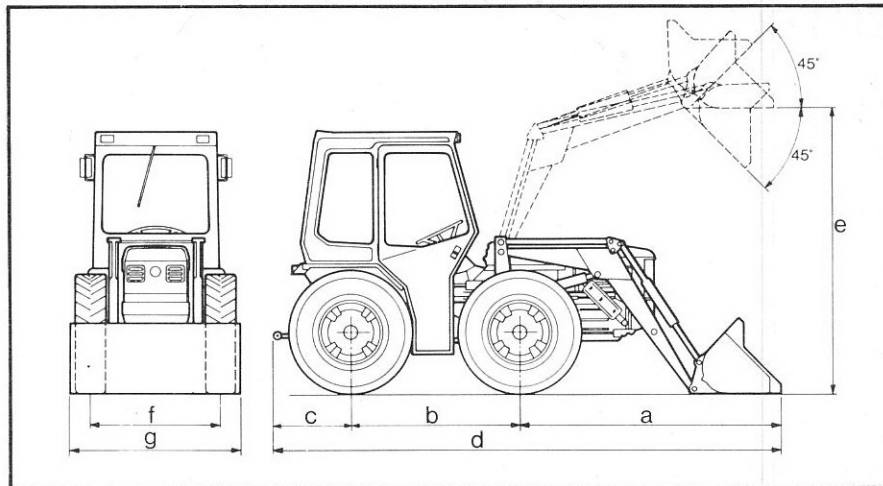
Schéma et dimensions du tracteur à pelle mécanique.
